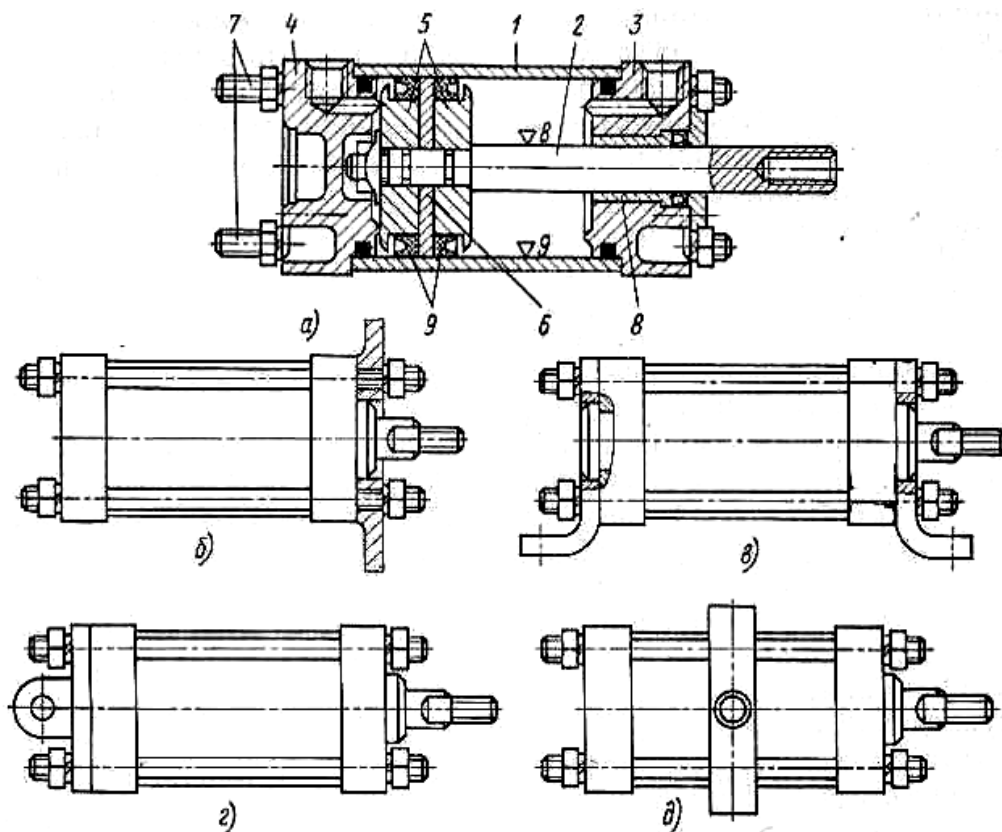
Пневмоцилиндры с креплением удлиненными стяжками
